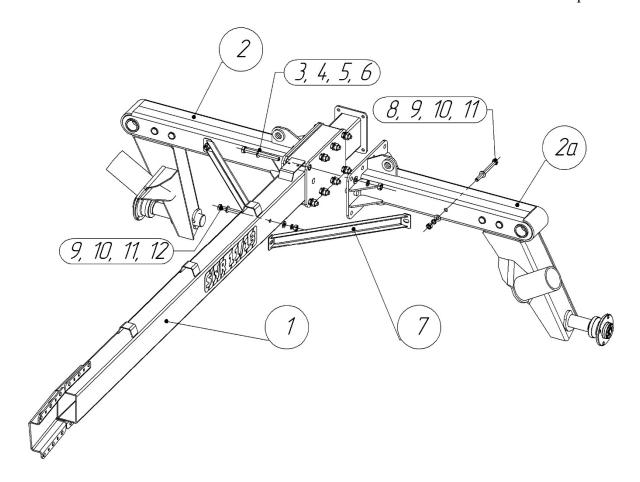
Установка балки опорного колеса Для установки балки опорного колеса Вам потребуется нижеприведенный список узлов и ЗИП
